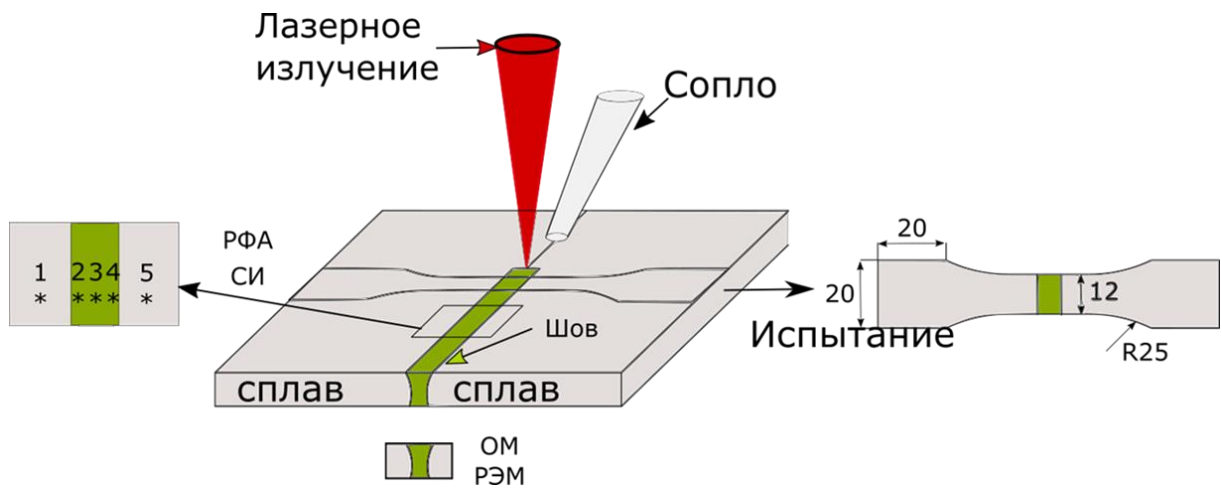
Схема лазерной сварки и подготовки образцов для исследований.
